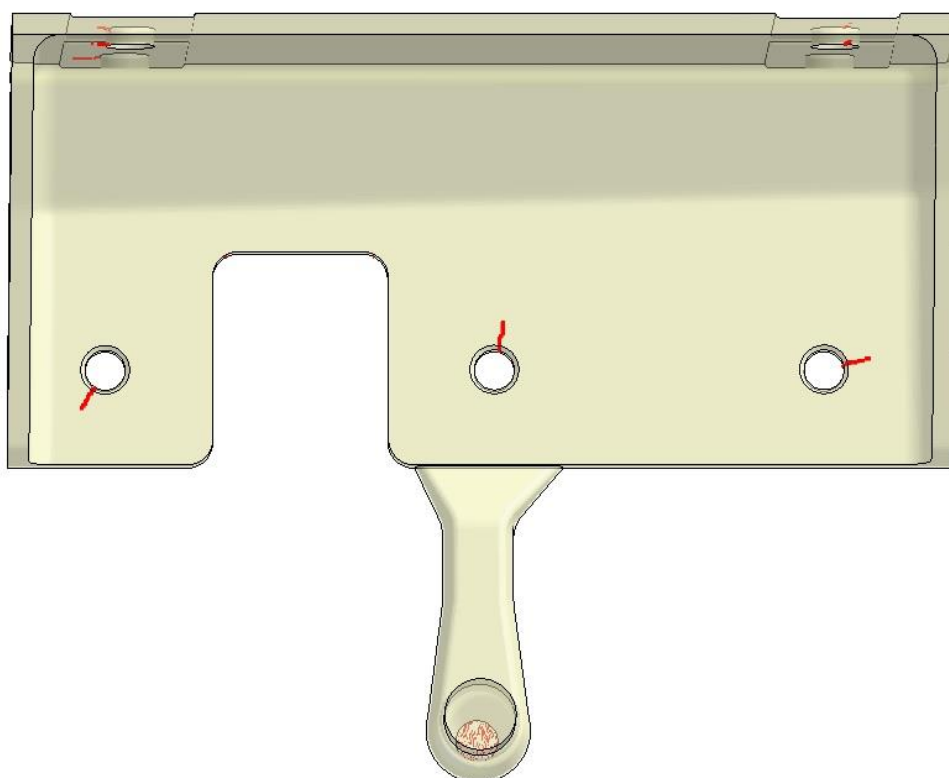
Linhas de soldadura junto dos furos criados pela bucha.
